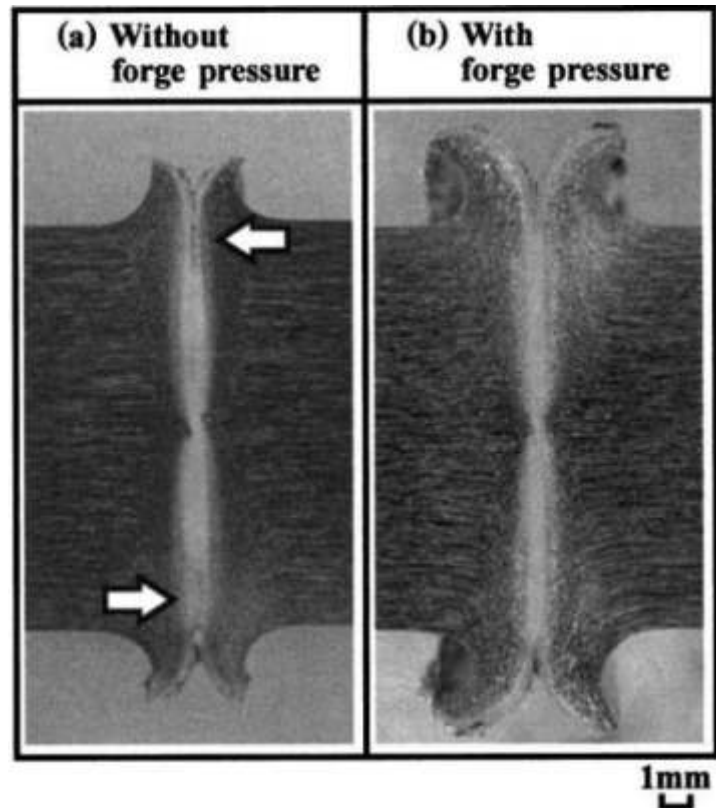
Sección transversal de dos uniones; a) soldadura sin carga de forja, b) soldadura con carga de forja [34]
